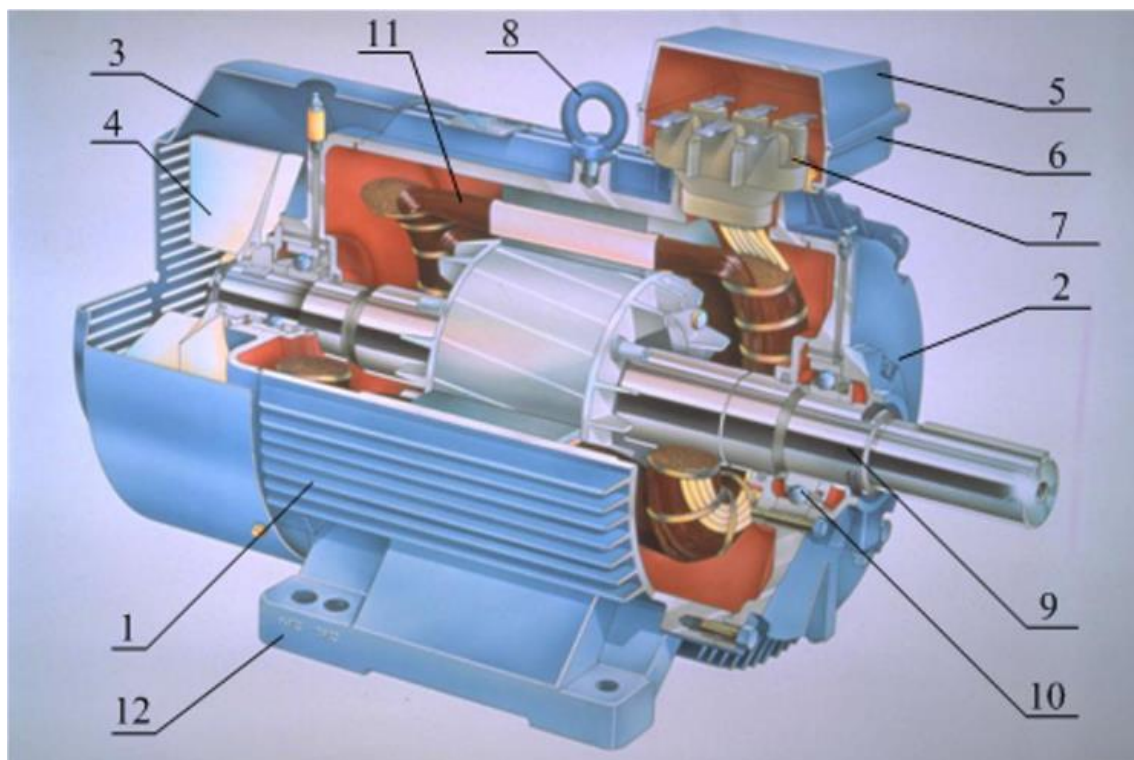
Будова трифазного асинхронного двигуна з короткозамкнутим ротором: 1 – статор; 2 – підшипниковий щит; 3 – кришка вентилятора; 4 – вентилятор; 5 – кришка; 6 – клемна коробка; 7 – клемна панель; 8 – рем-болт; 9 – ротор; 10 – підшипник; 11 – обмотка статора; 12 –лапи
